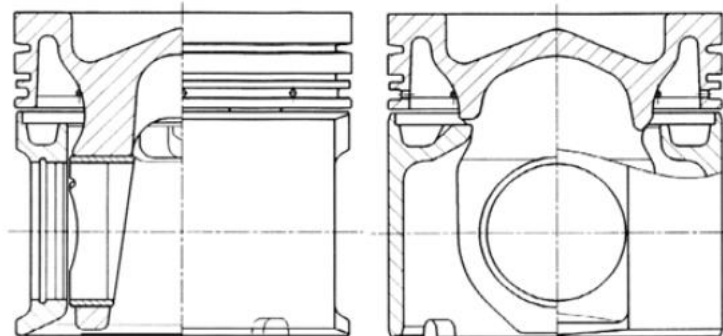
Klasické provedení pístu vznětového motoru nákladního automobilu [5]
